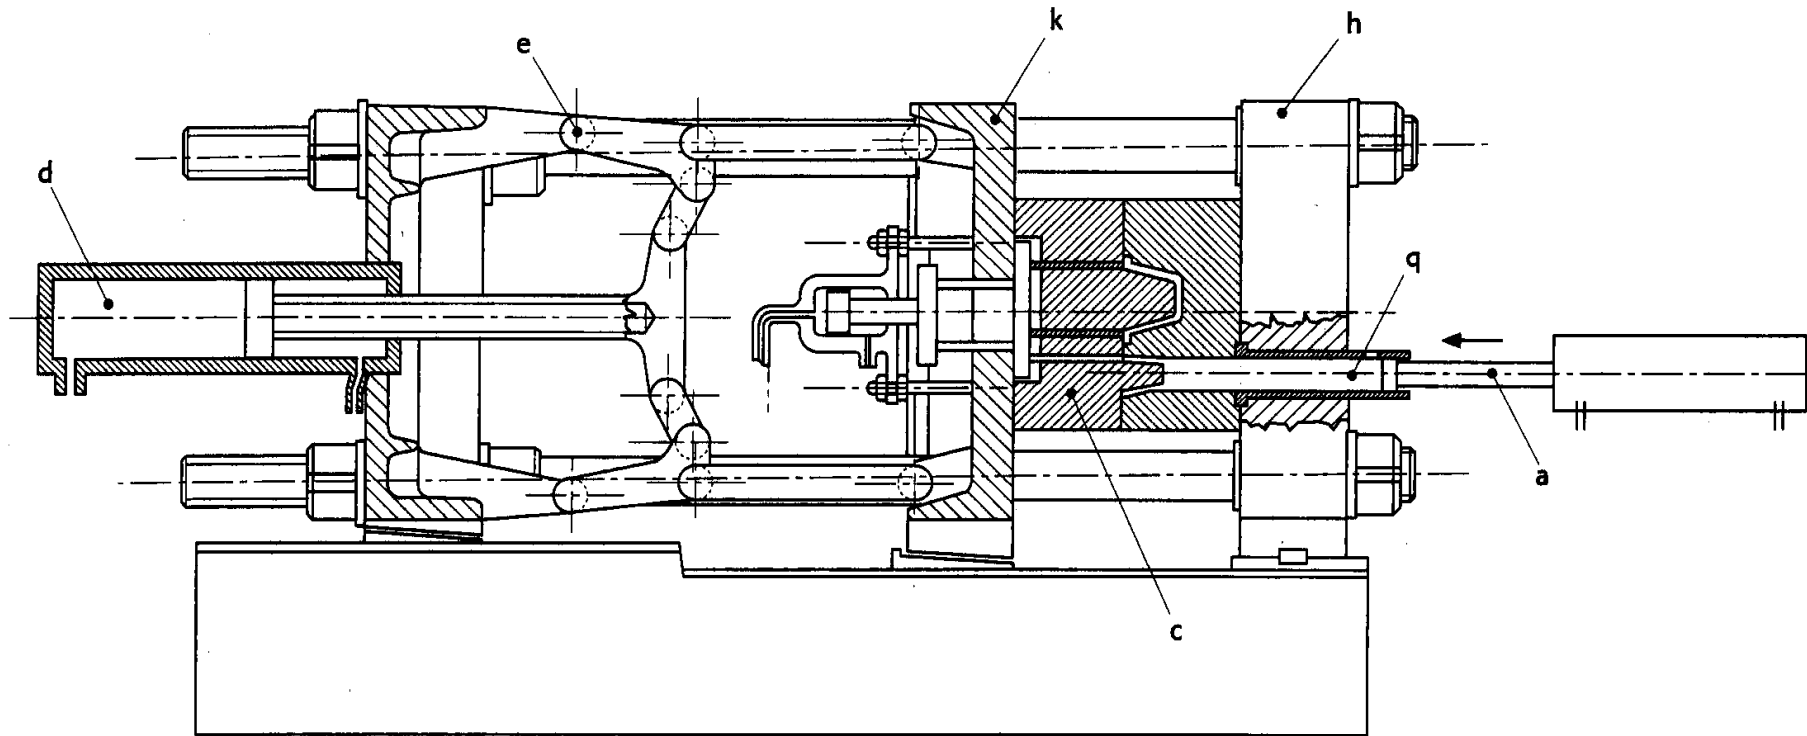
Macchina per iniettofusione a camera calda a pistone tuffante.
